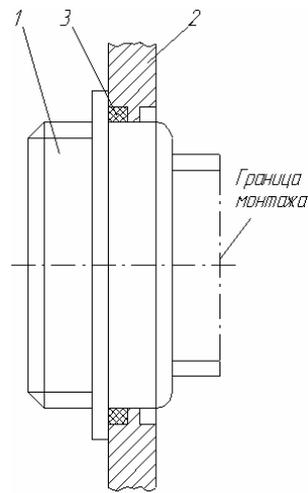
Герметизация вилки соединителя РСГ с помощью уплотнительной прокладки: 1 – вилка разъёма; 2 – корпус блока; 3 – уплотнительная прокладка
